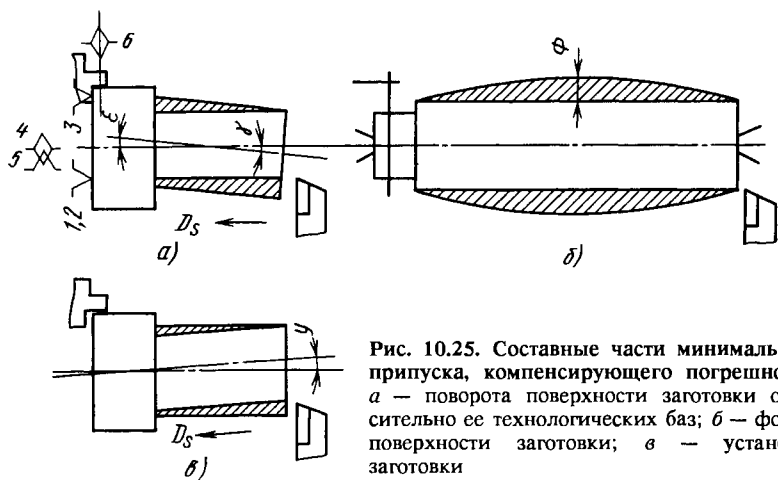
Составные части минимального припуска, компенсирующего погрешности: а — поворота поверхности заготовки относительно ее технологических баз; б — формы поверхности заготовки; в — установки заготовки
